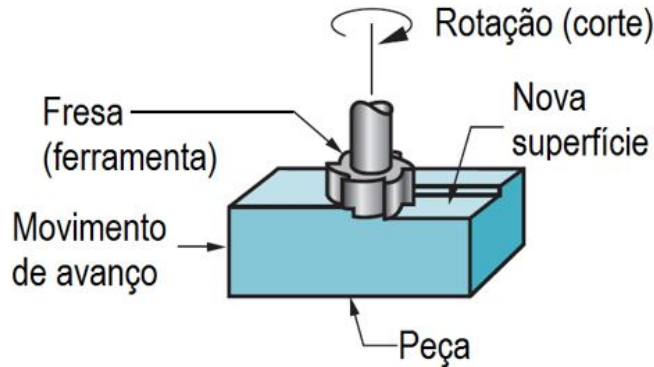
Exemplo de fresagem frontal ou de topo [5].
